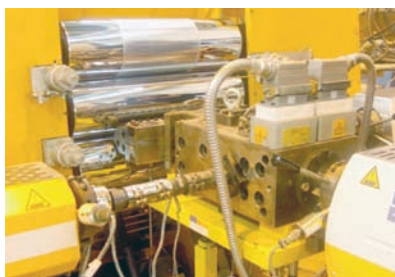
Línea coextrusión lámina plana planta piloto Aimplas.
